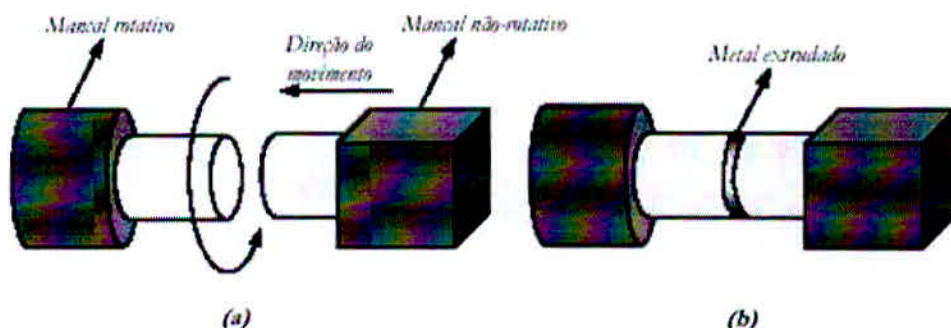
Processo de soldagem por fricção: (a) aproximação, (b) após soldagem.
